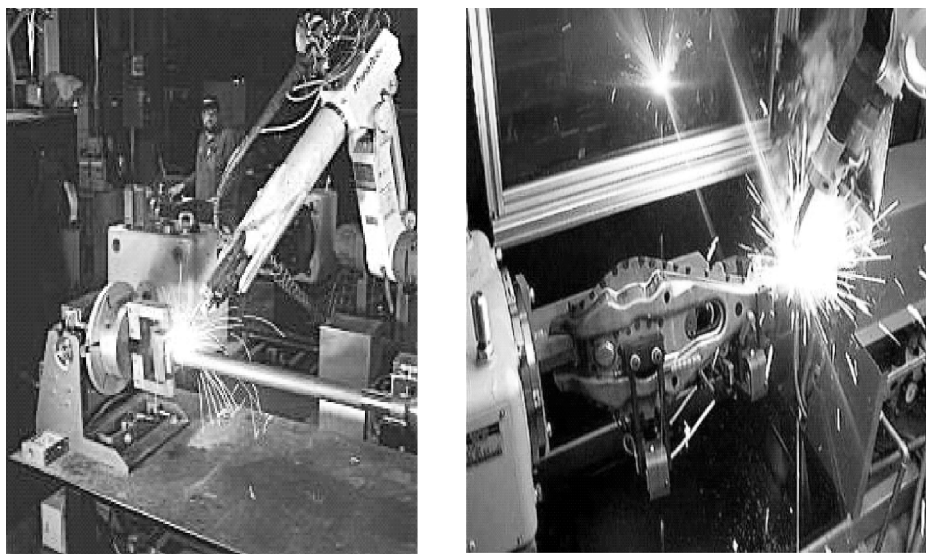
传动轴等零部件的旋转“车床”型焊装夹具
